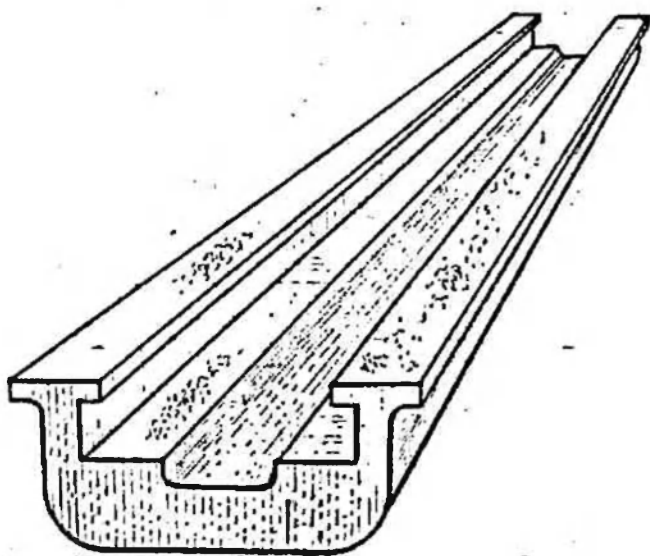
При механической обработке отливки вскрылись усадочные раковины.
